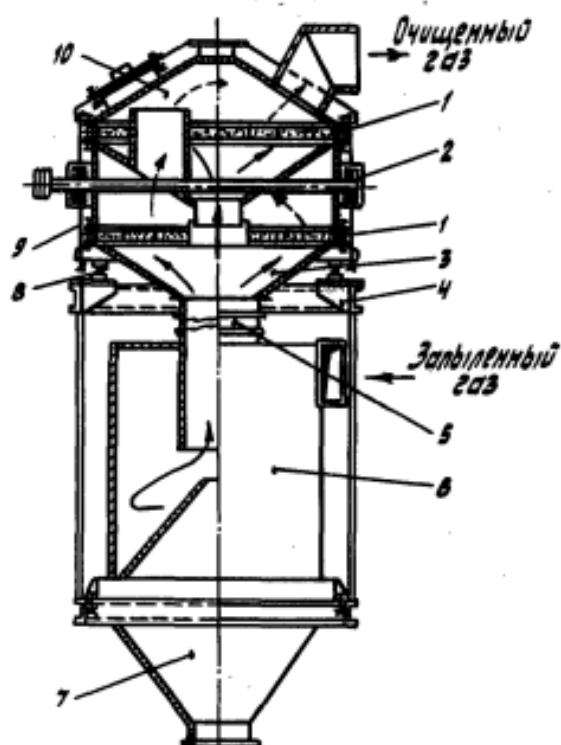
Фильтр-циклон ФЦЗ-6: 1 — кассета с фильтрующим зернистым слоем; 2 — виброустройства; 3 — основание; 4 — рамы с опорным поясом; 5 — рукава; 6 — циклонный элемент; 7 — бункера уловленной пыли; 8 — пружины; 9 — шпильки; 10 — крышка
